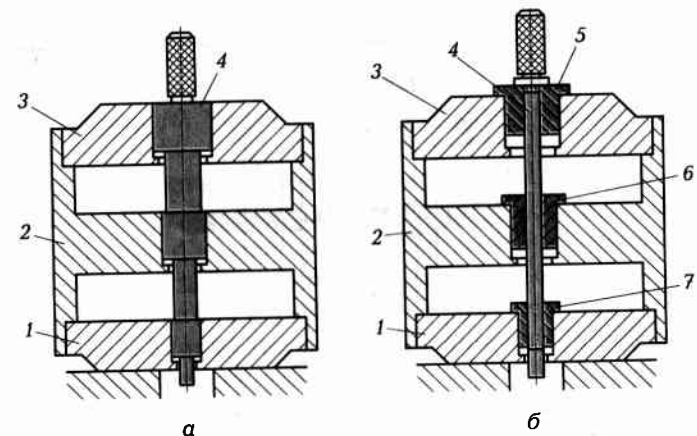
Схема контроля соосности жесткими калибрами:
